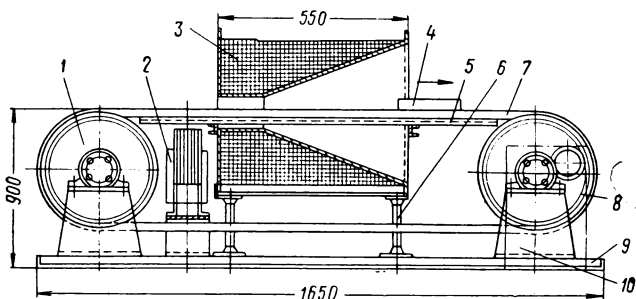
Устройство для размагничивания деталей роликовых подшипников:
